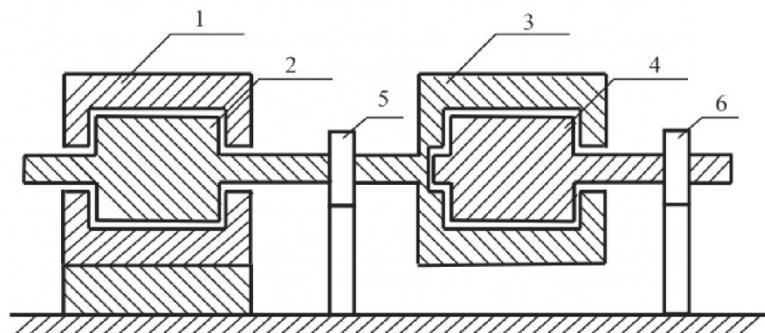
Конструктивная схема сдвоенного двигателя: 1 – статор первого двигателя; 2 – ротор первого двигателя; 3 – статор второго двигателя; 4 – ротор второго двигателя; 5, 6 – подшипниковые опоры
